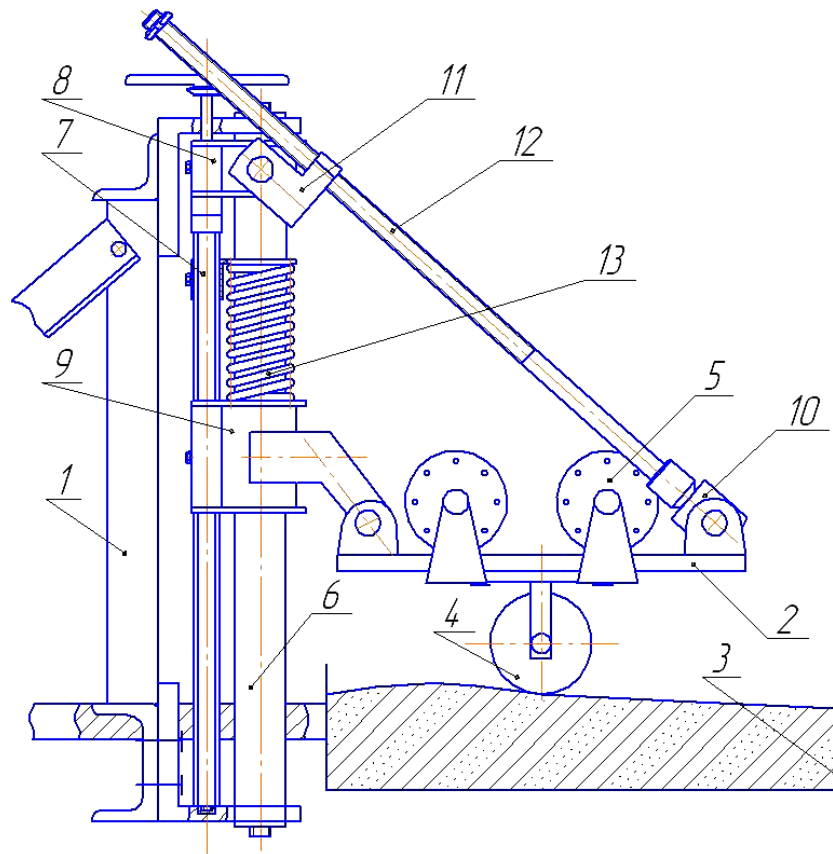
Схема підвісного обладнання лабораторного стенда МЗР
